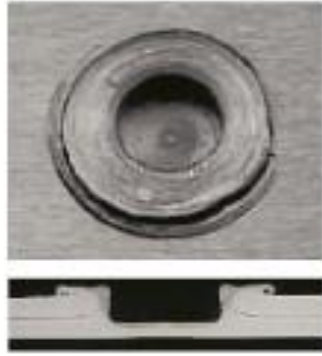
trou de soudure du a la soudure FSSW (4)
